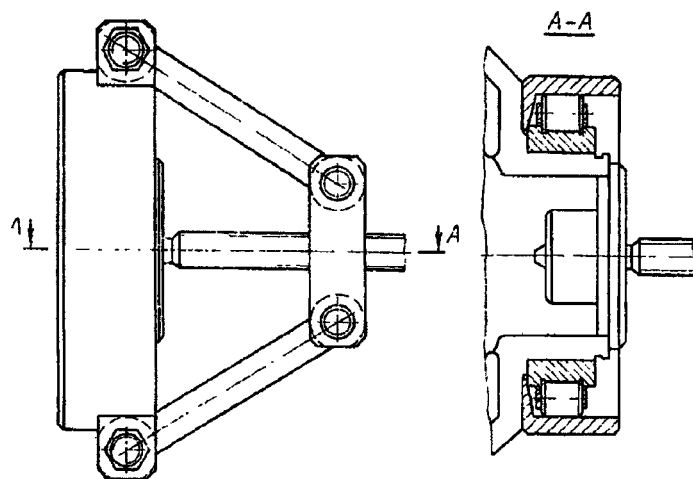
Снятие внутреннего кольца роликоподшипника зубчатого колеса низшей передачи привода заднего моста
